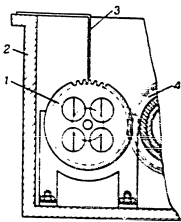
Проверка зазора для проверки шестерни редуктора.
